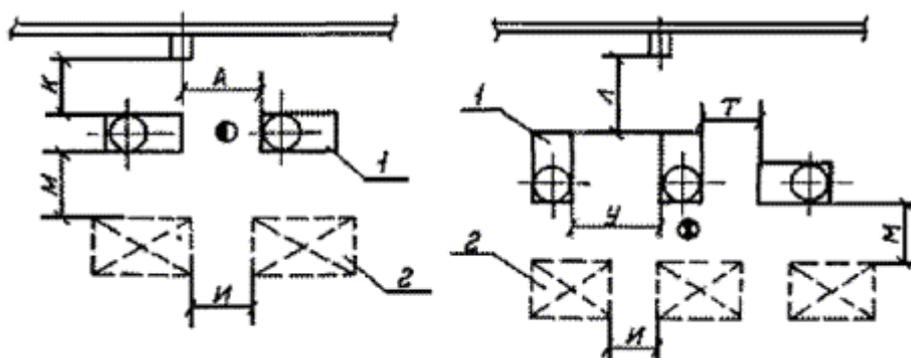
Размещение автоматов для сварки кольцевых швов:
